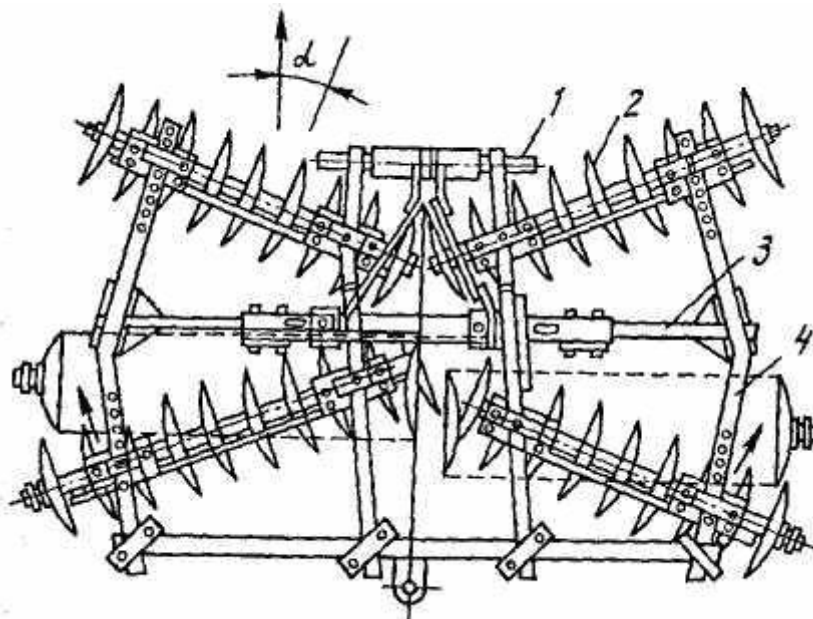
Дисковая борона БДН-2.2: 1 - навеска; 2 - батарея дисков; 3-рама; 4- брус с устройством для регулировки угла атаки
